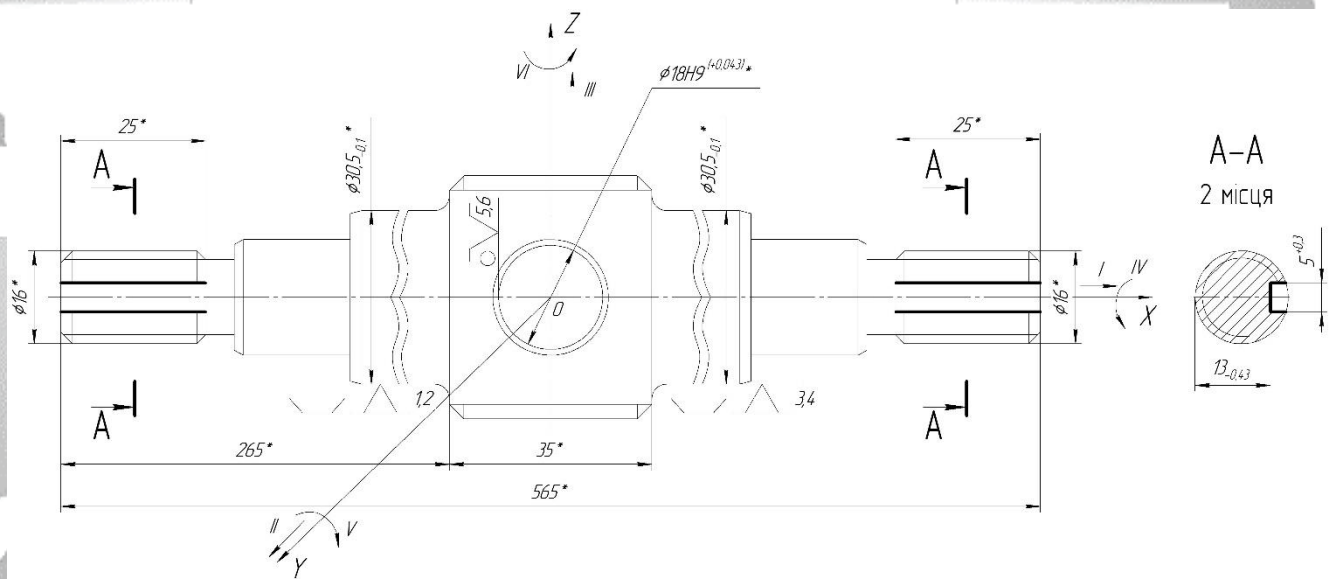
Схема базування заготовки на фрезерній з ЧПК операції
